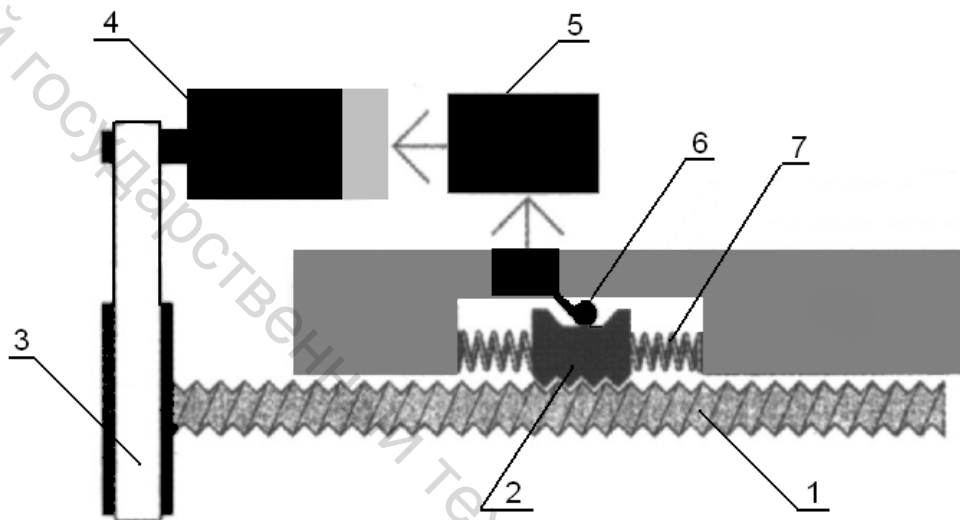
Привод с шариковой винтовой и ременной передачами:
